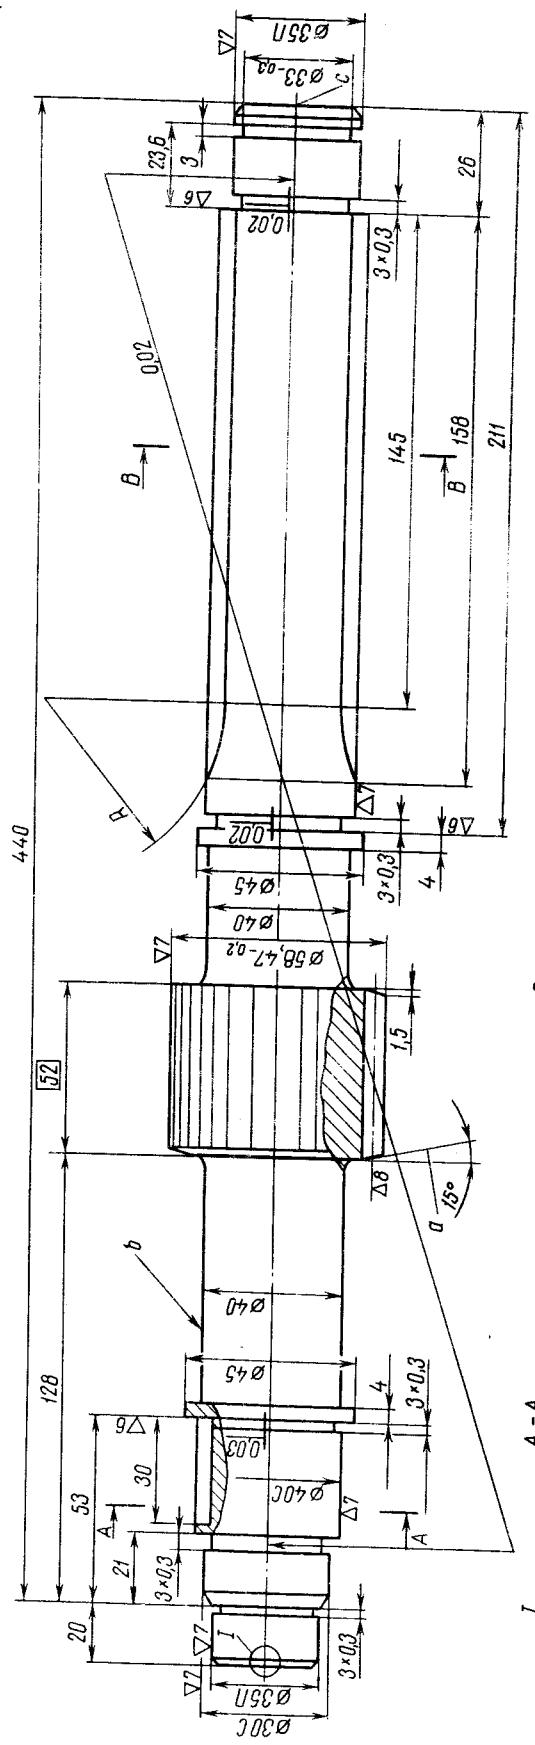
Вал-шестерня № 2П1536 (материал — сталь 18ХТ ГОСТ 4543-71):
